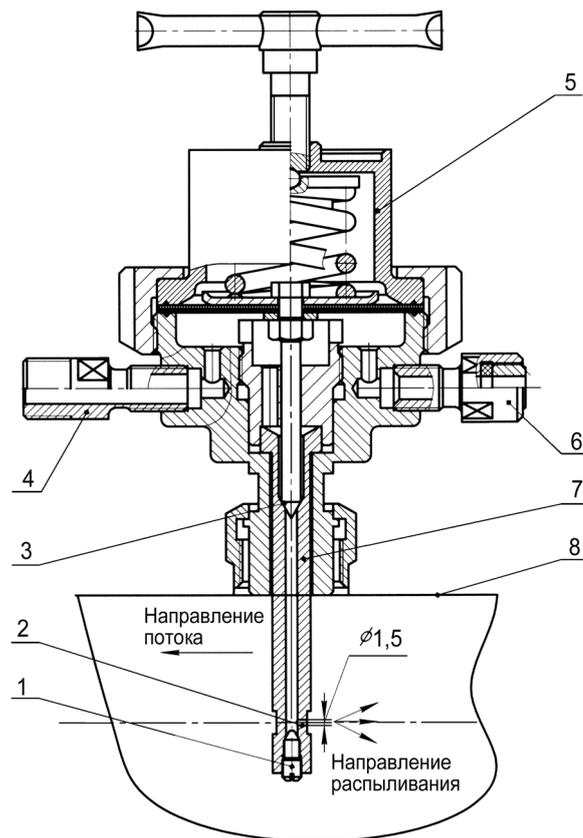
Схема дозатора и форсунки: 1 – резьбовая пробка; 2 – калиброванное отверстие; 3 – клапан; 4 – входной штуцер; 5 – дозатор; 6 – предохранительный клапан; 7 – трубка для подвода раствора желатина; 8 – трубопровод
